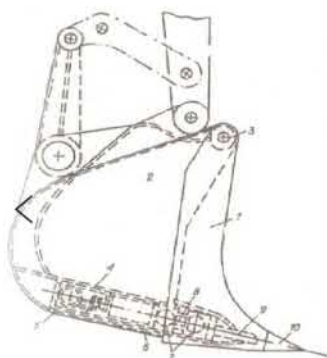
Ковш с вибрирующей режущей кромкой по патенту № 33228426 ФРГ
